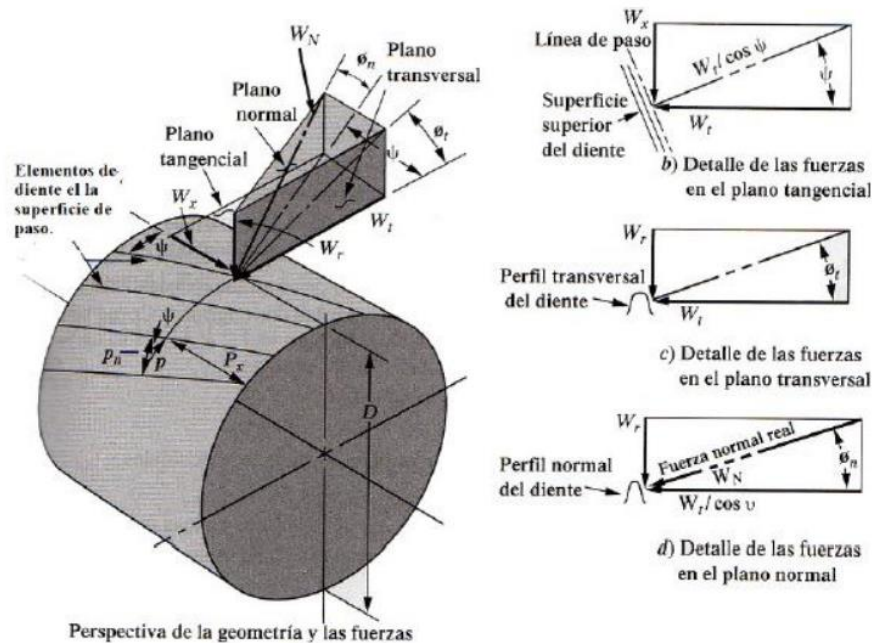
Perspectiva de las fuerzas en un engranaje helicoidal [8]
